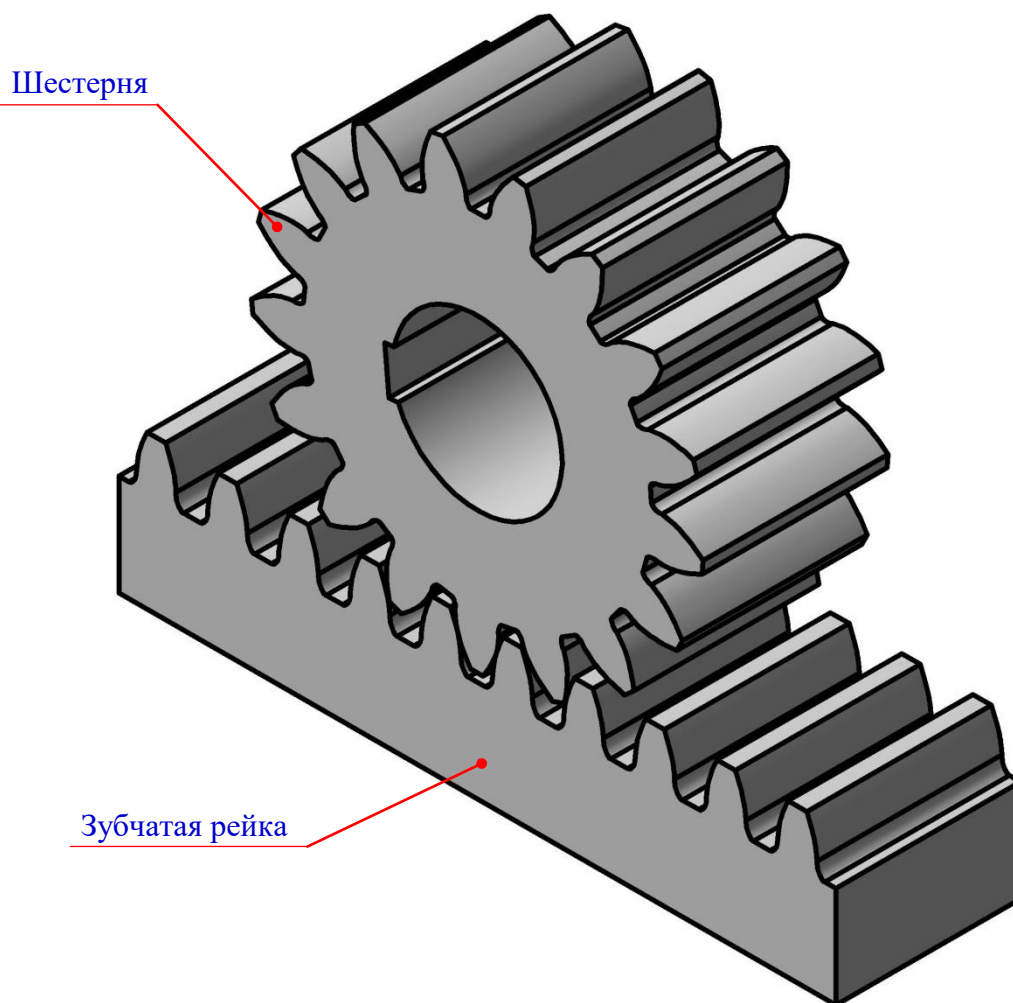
Реечная зубчатая передача предназначена для *преобразования* одного вида движения в другой: вращения зубчатого колеса (шестерни) в поступательное перемещение зубчатой рейки и наоборот – поступательного перемещения зубчатой рейки во вращение зубчатого колеса (шестерни)
